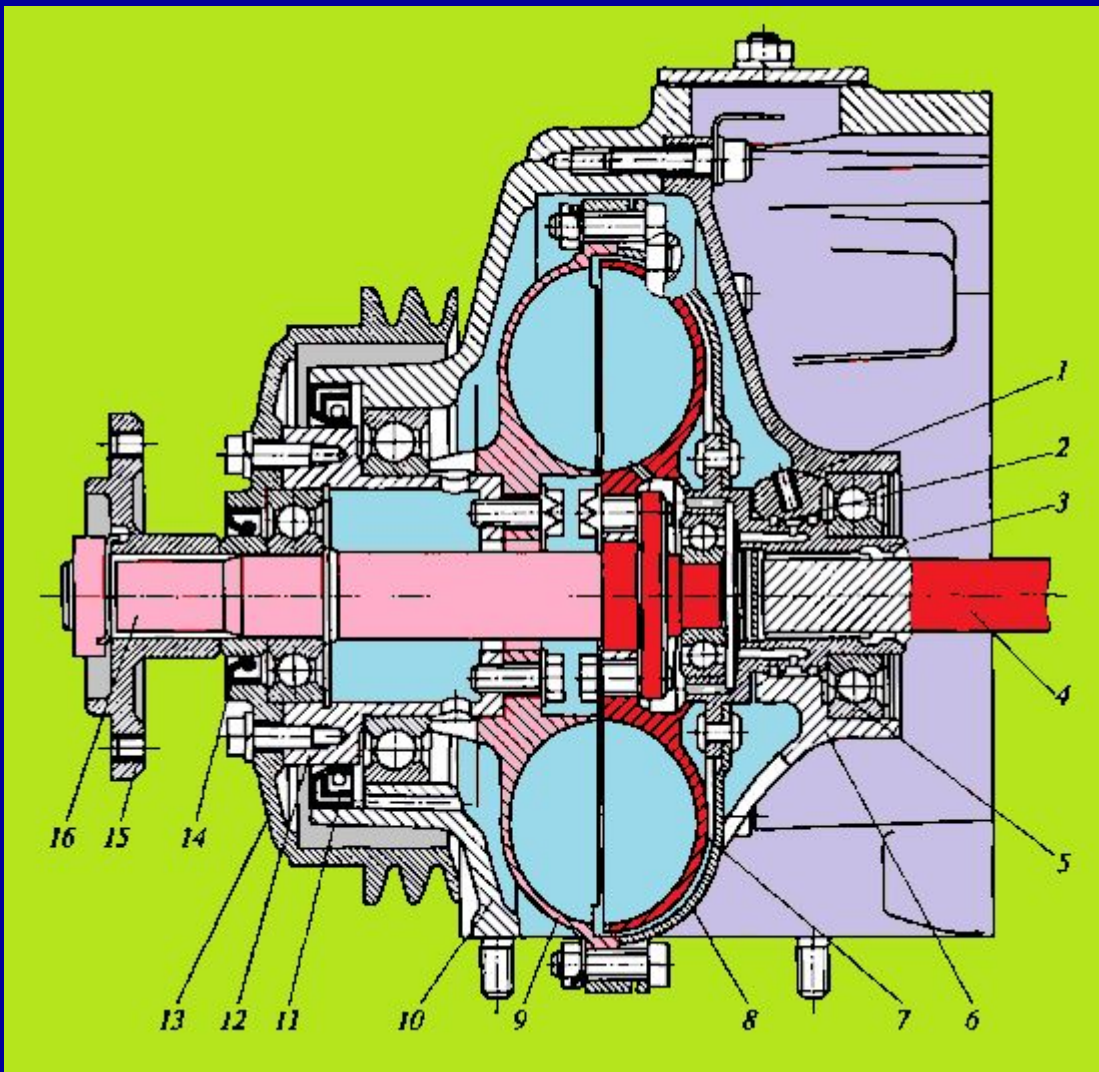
Гидромуфта привода вентилятора со шкивом генератора в сборе:
